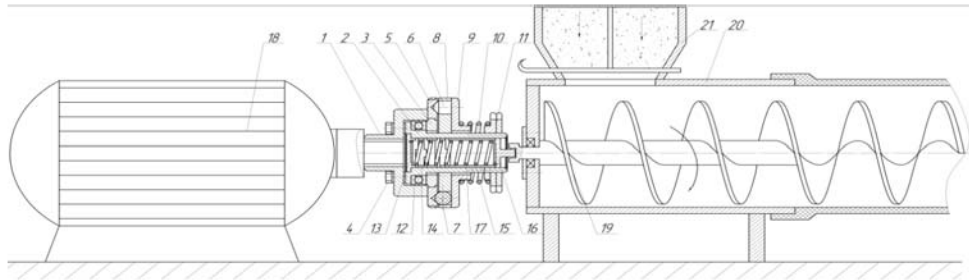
Гвинтовий конвеєр обладнаний пружно-запобіжною муфтою
